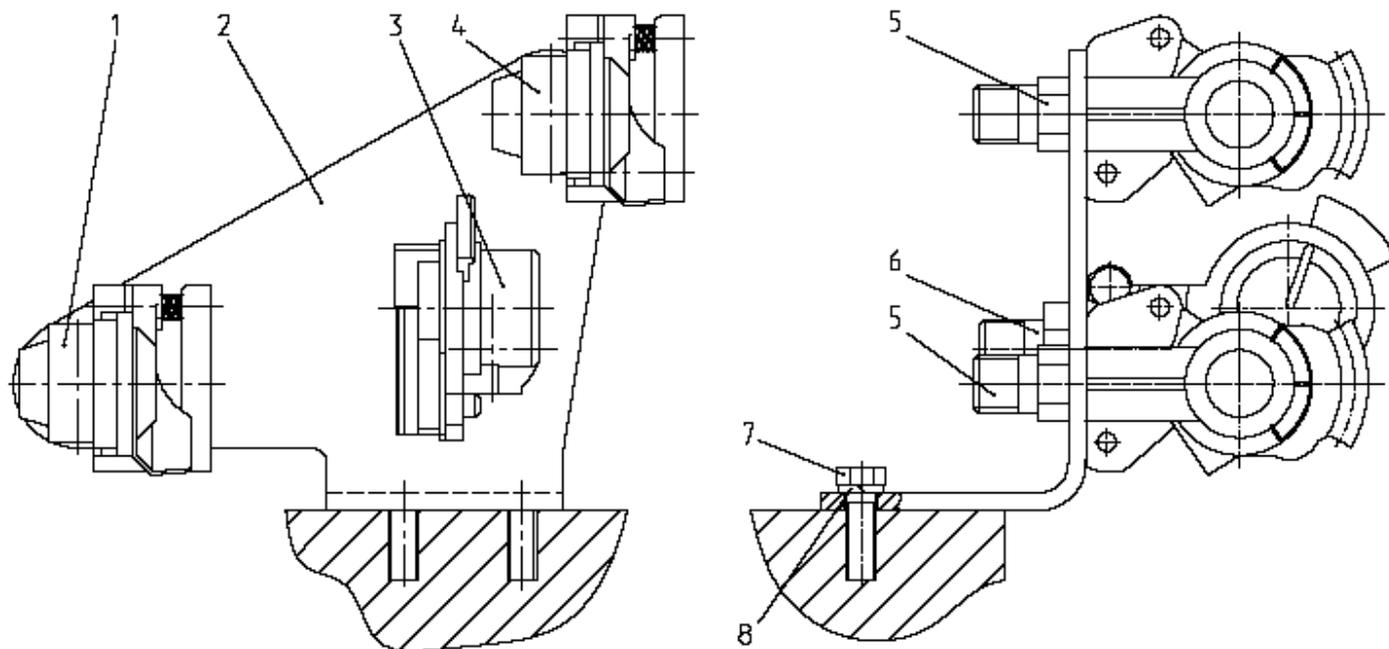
Установка головки соединительной (комбинированный пневмопривод тормозов прицепа)
